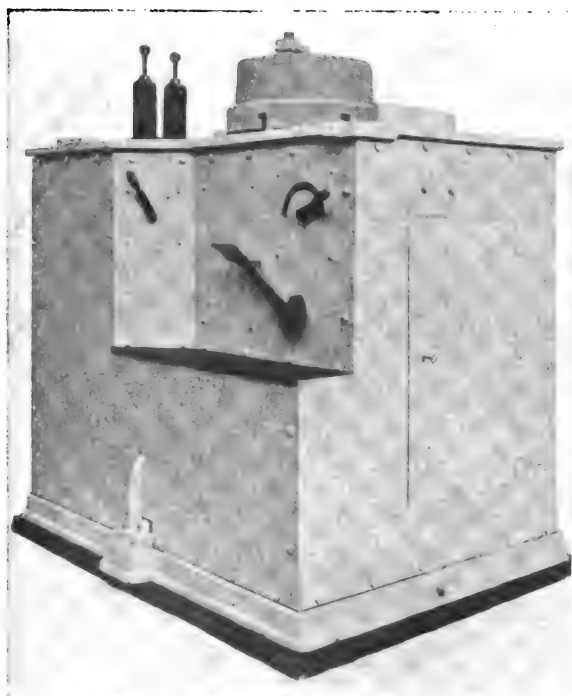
Vue d'ensemble du bloc à tréfiler.
